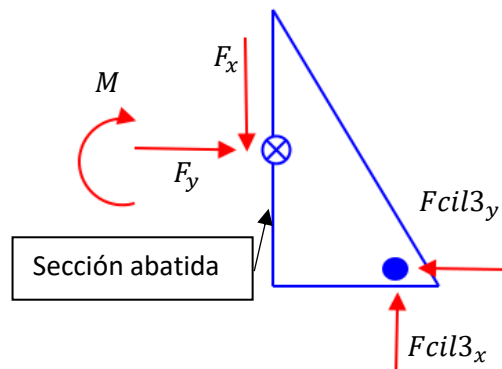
(2): DSL de cordón de soldadura
